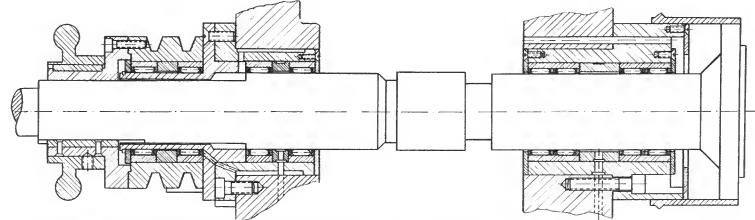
Werkstückspindellagerung einer Innenschleifmaschine mit Oszilliereinrichtung (Hess, Werkzeug- und Apparatebau)
